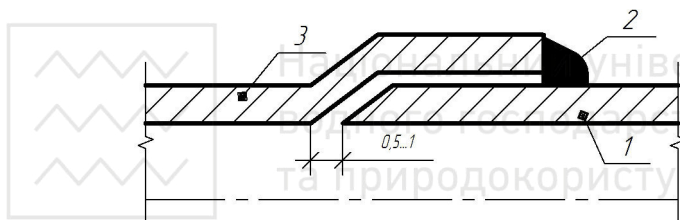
Зварювання пластмасових труб в розтрубі нагрітим газом: 1-з'єднувальний гладкий кінець труби, 2- зварний шов, 3-з'єднувальний кінець труби з розтрубом.
